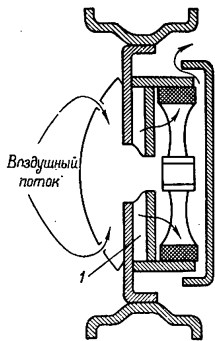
Схема вентиляции колесного тормоза; 1 — лопатки вентилятора
